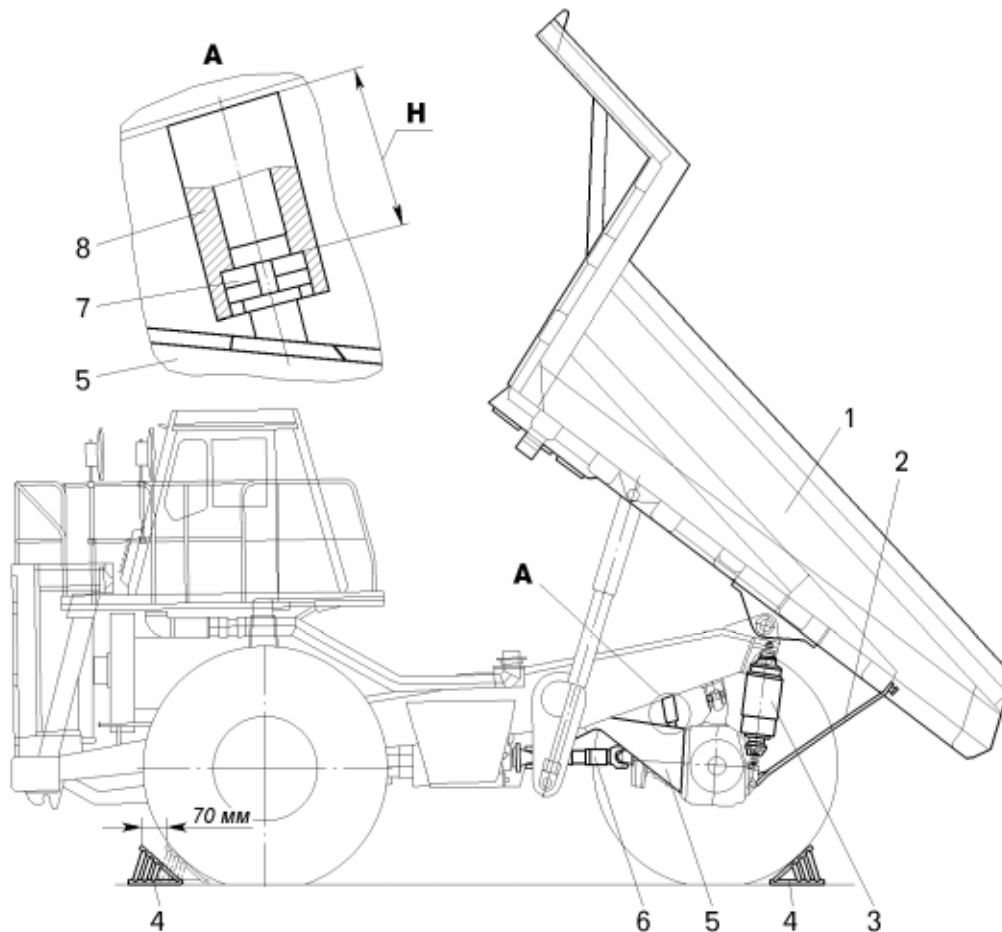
Разборка и сборка центрального шарнира задней подвески с поднятой платформой:
